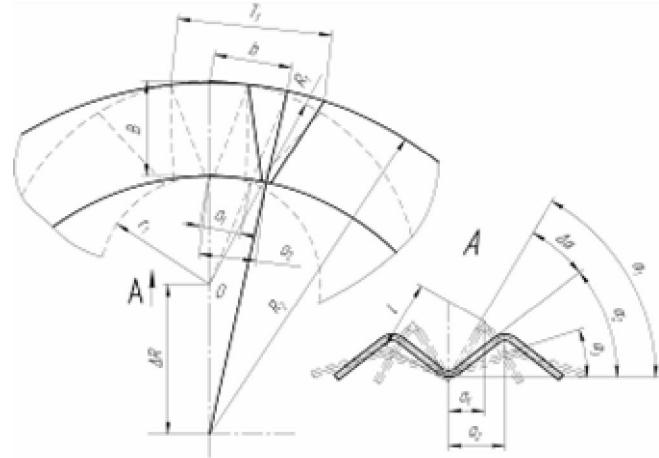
Розрахункова схема відпружинення профільної гвинтової заготовки
